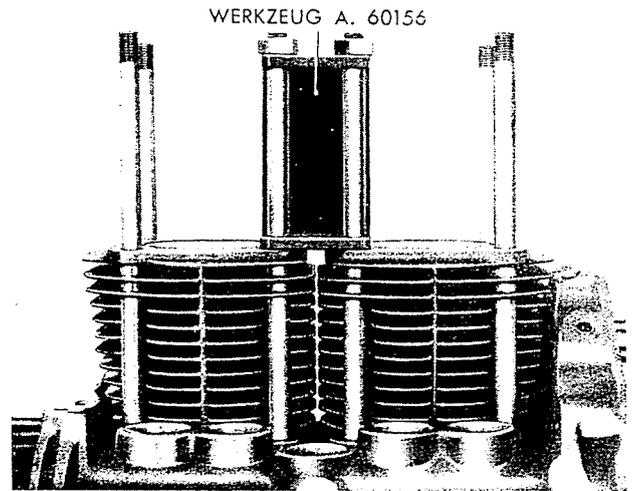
Werkzeug A. 60156 zur Sicherung der Zylinder.
